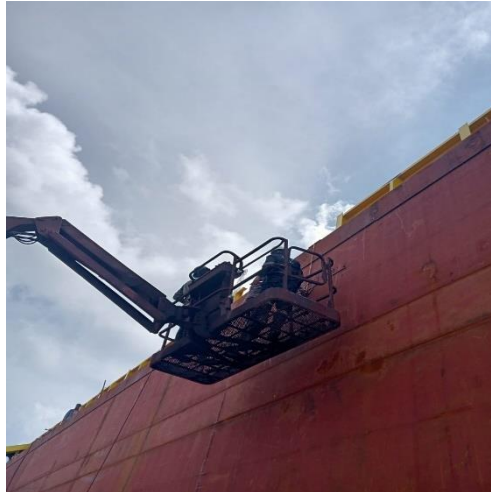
2 *Inspect welding* panel *main deck
